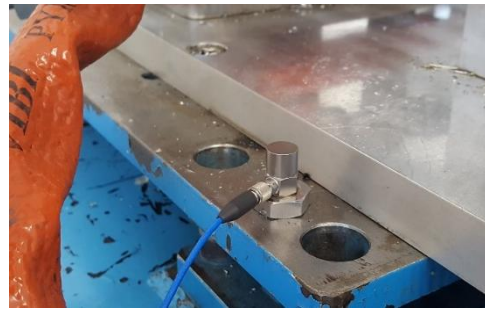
Accelerometro PCB C352C33 posto sulla piastra di fissaggio del piano rettificato
